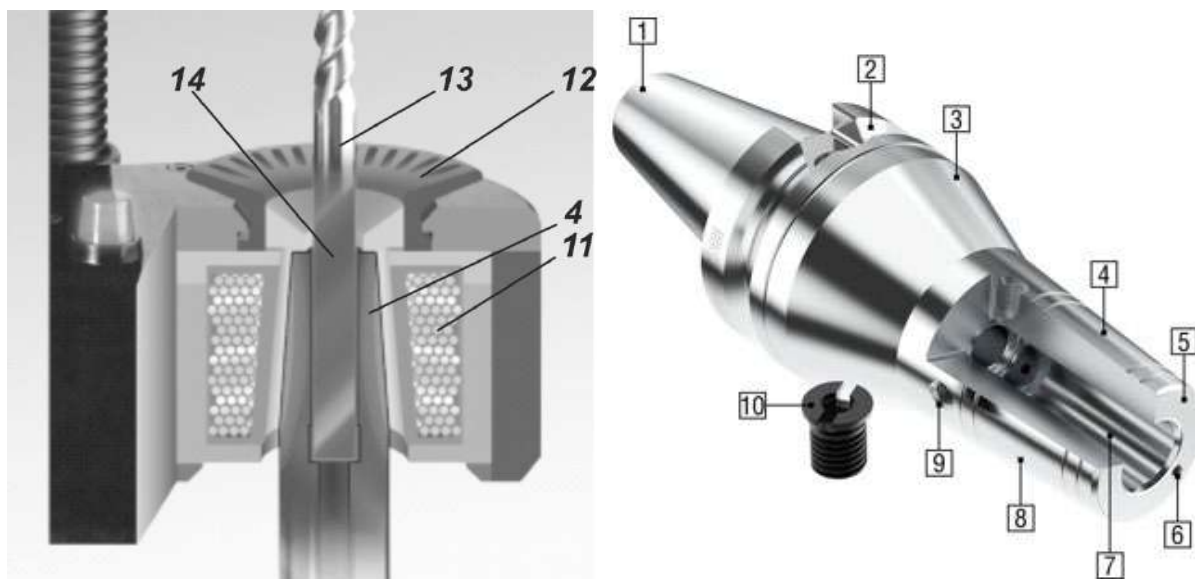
Принципова конструкція та схема роботи термооправки фірми SECO
